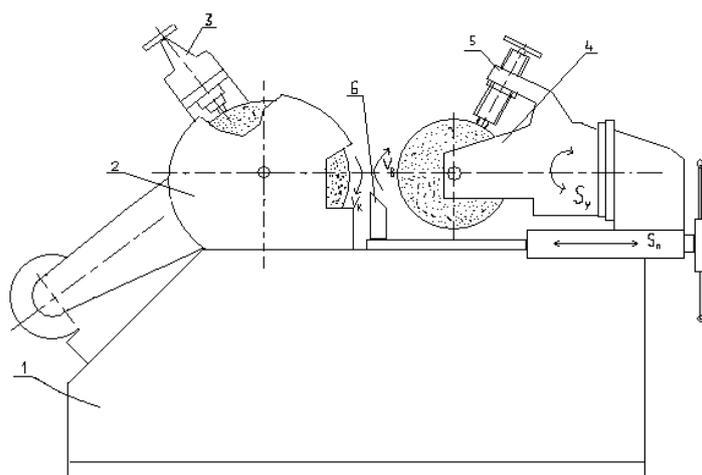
Схема бесцентрово-шлифовального станка:
